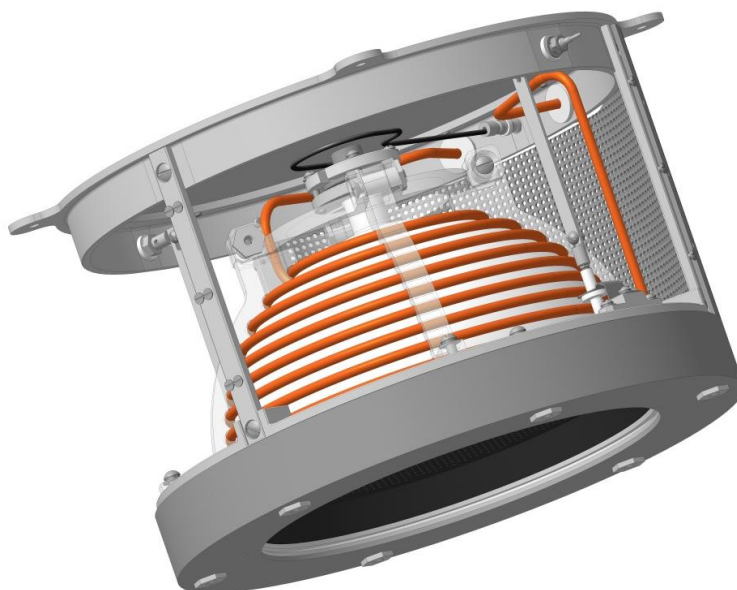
Лабораторный образец ЛО ВЧИД – 16
